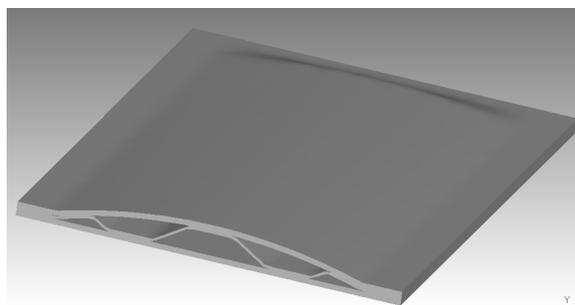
МКЭ – модель трехслойной конструкции в разрезе
